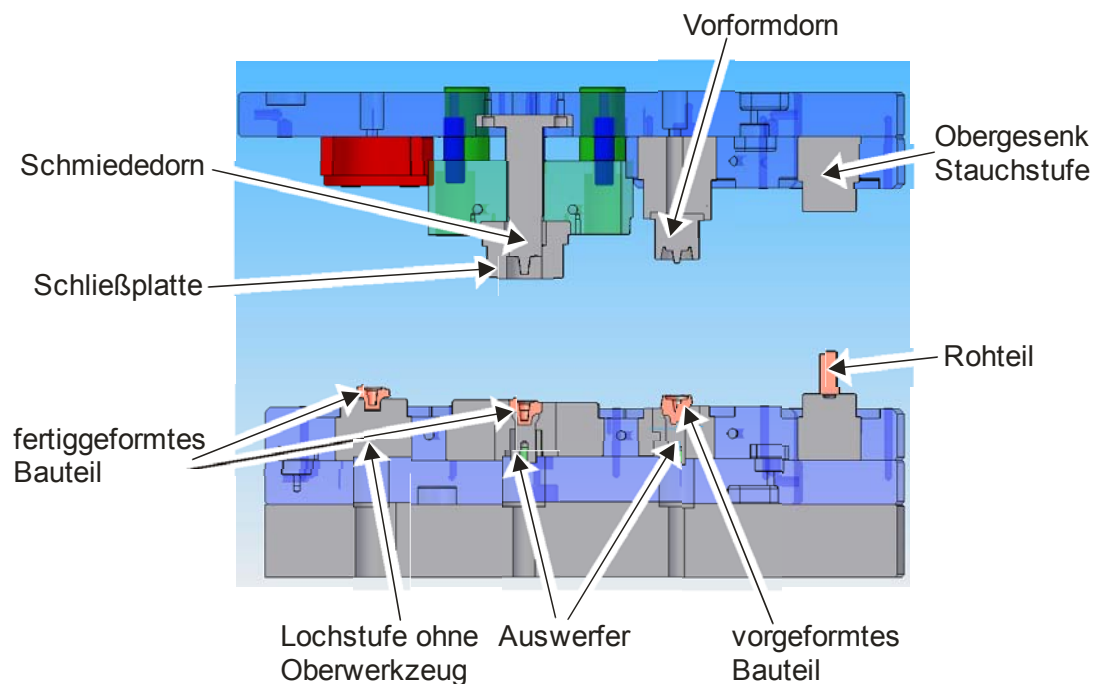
3D-Ansicht des gesamten Werkzeugsystems
